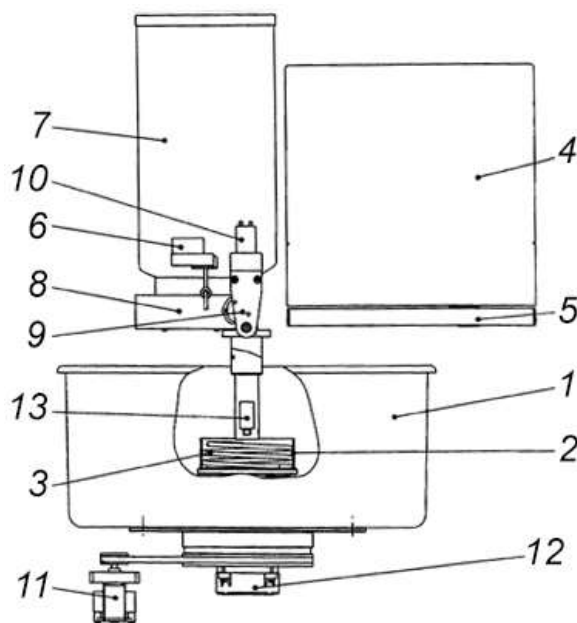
Схема апарата для готування цукрової вати з механізмом видачі паличок
